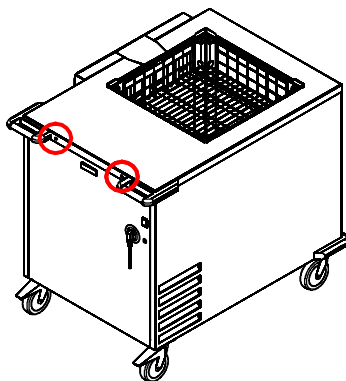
Lage der Befestigungsschrauben (Vorderseite)
